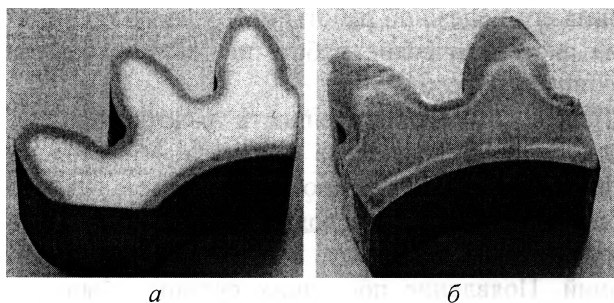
Фотография макрошлифа фрагмента детали сателлит: а — из стали 20ХНЗА, прошедшей операцию цементации, б — из стали 60ПП с объёмно-поверхностной закалкой
